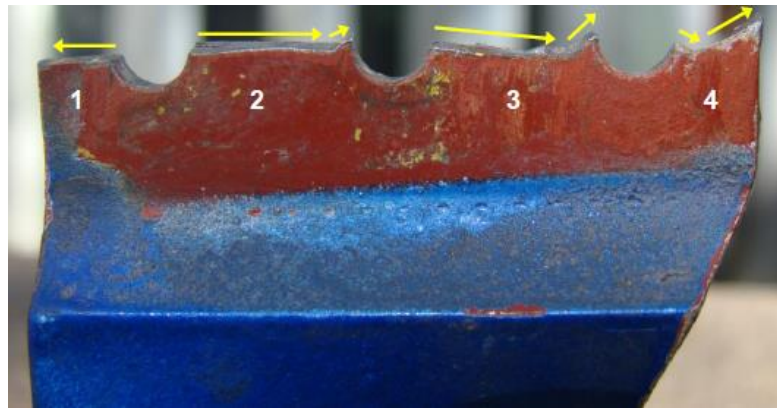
Cara de fractura del herraje derecho. Fuente: investigación JST
